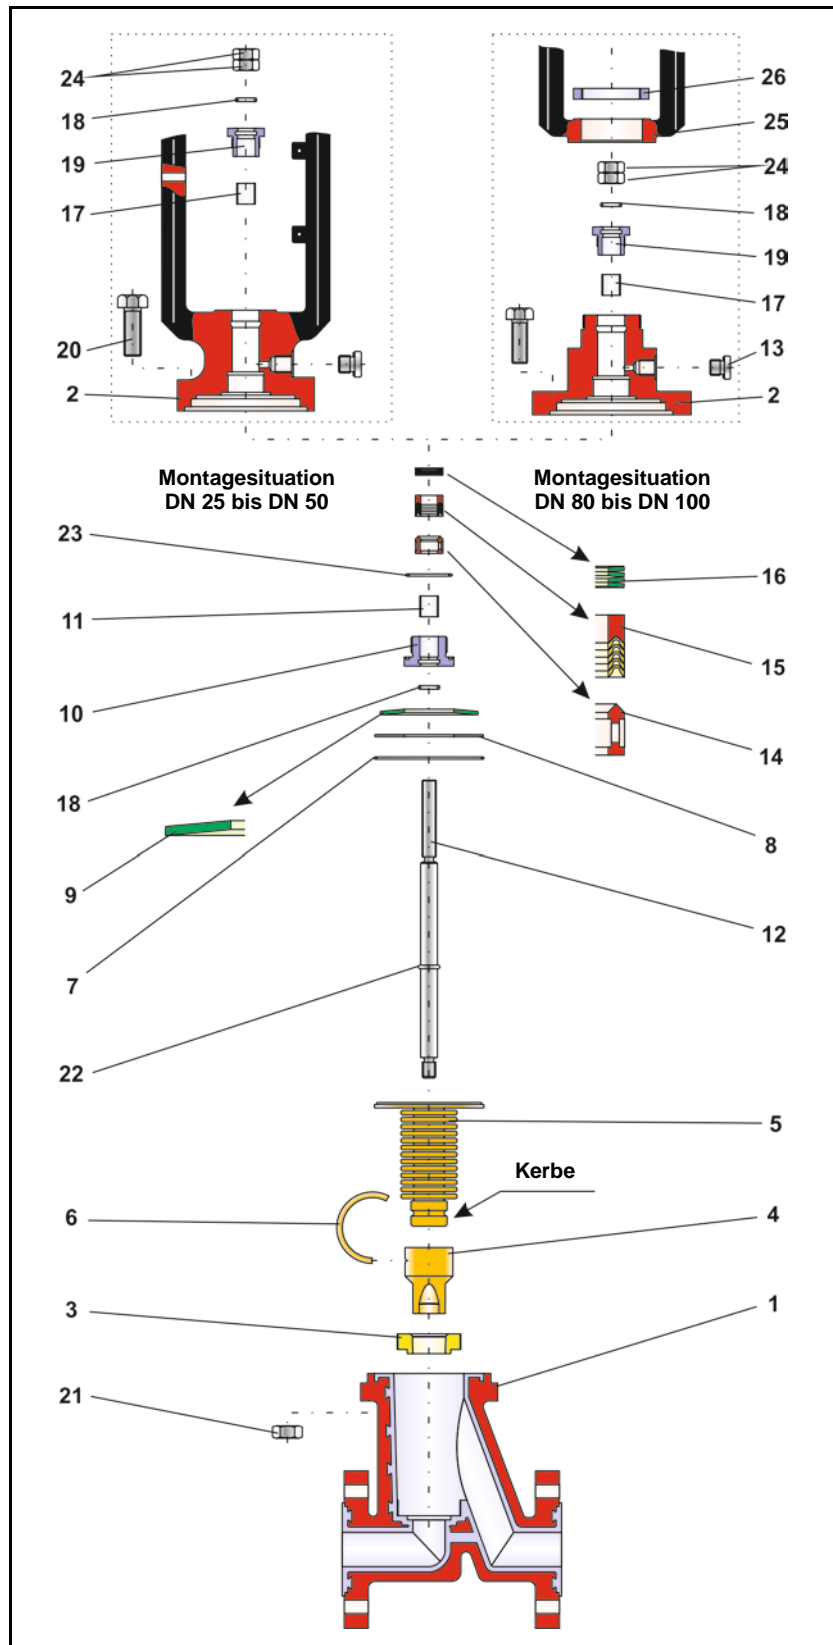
Explosionszeichnung des Stellventils BR 01b, ab Baujahr 2006
